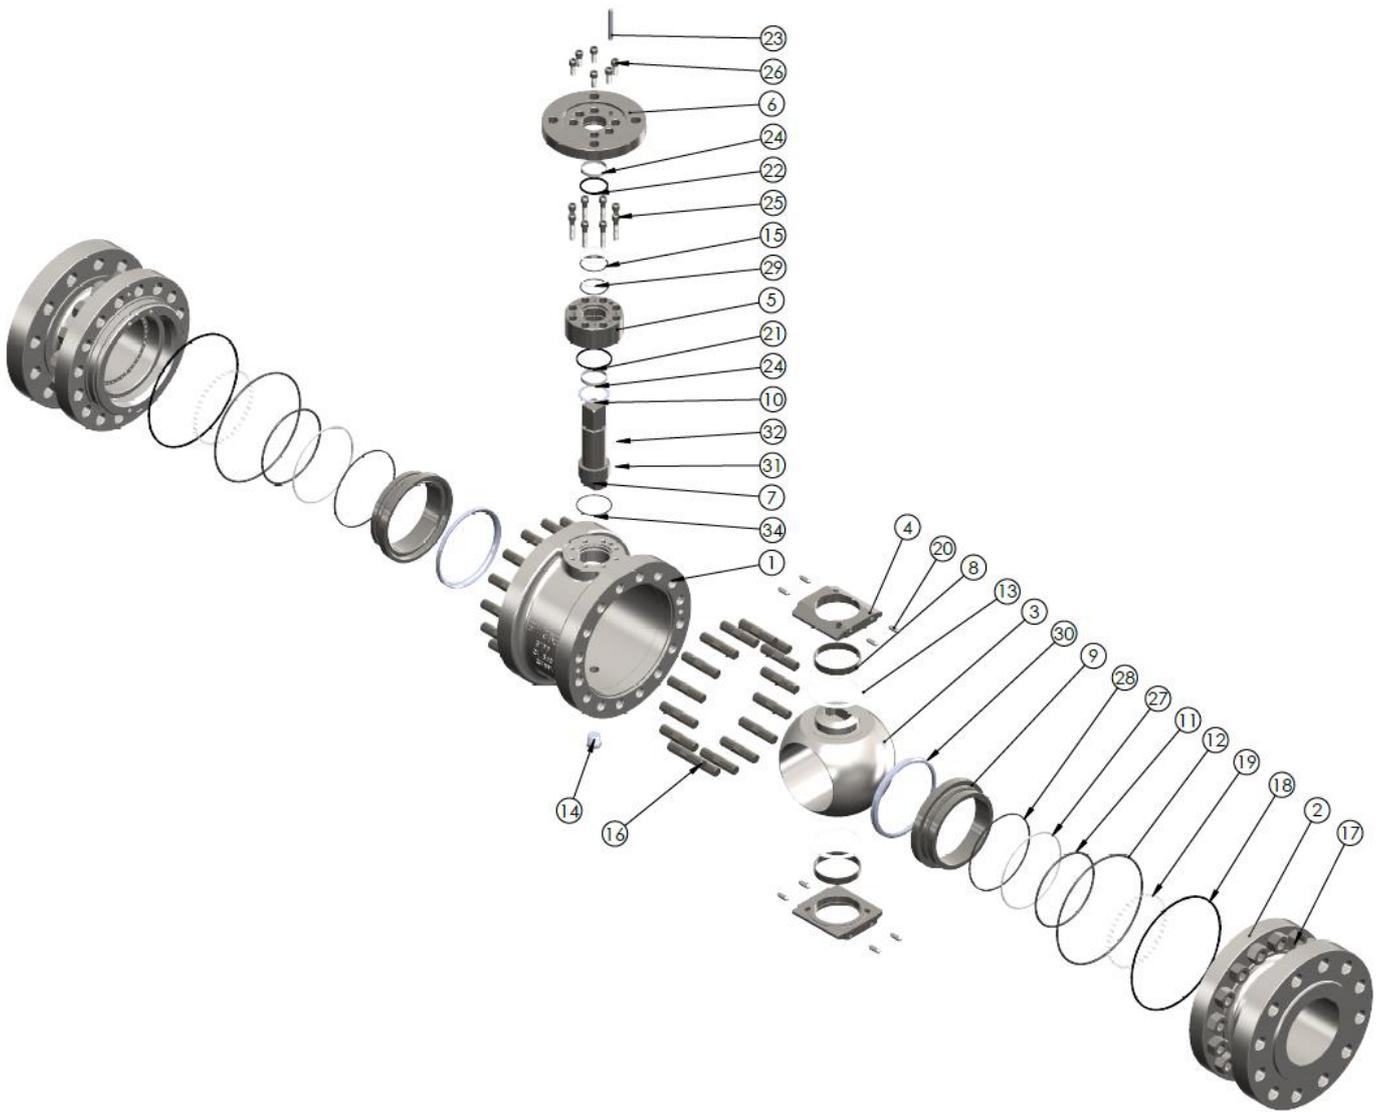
Vista explodida da Válvula de Esfera Trunnion 6"PP e acima (Sequência de montagem)
